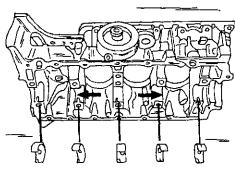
Вкладывание вкладышей коренных подшипников. Два вкладыша со смазочными отверстиями устанавливаются в отверстия. отмеченные стрелками.
